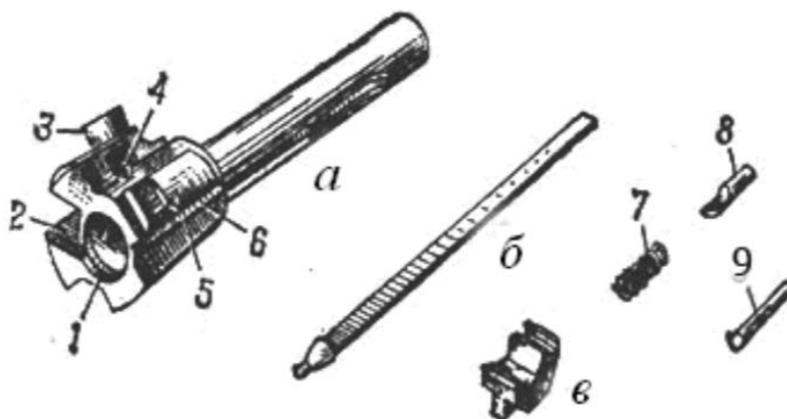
Затворная рама с газовым поршнем: 1 – канал для затвора; 2 – предохранительный выступ; 3 – выступ для опускания рычага автоспуска; 4 – паз для отгиба ствольной коробки; 5 – рукоятка; 6 – фигурный вырез; 7 – паз для отражательного выступа; 8 – газовый поршень
